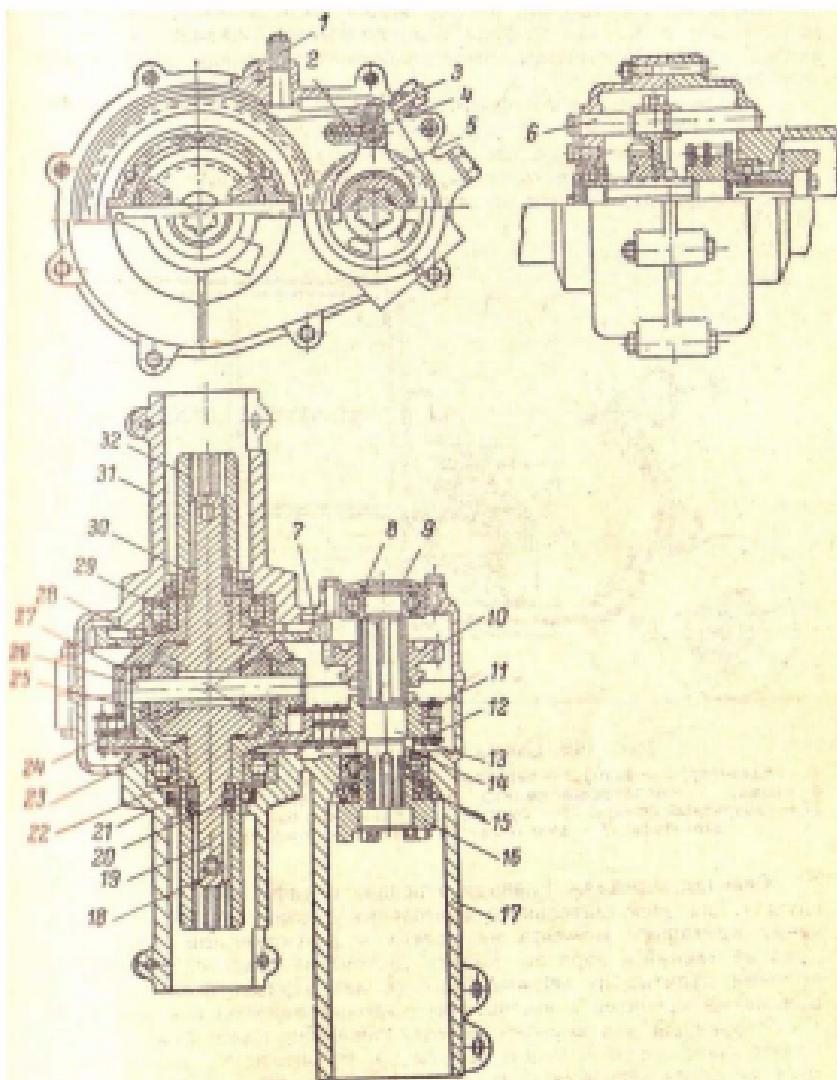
Главная передача грузового мотороллера „Витязь”:
